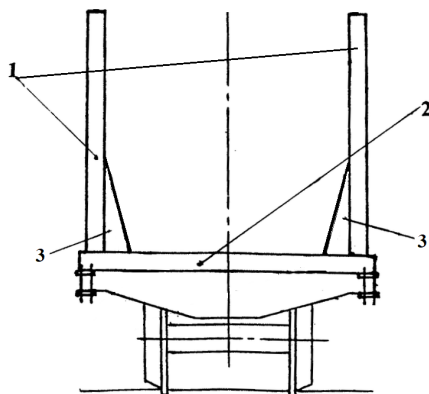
Схема поперечного сечения железнодорожной платформы со стойками, ограждающими штабель круглых лесоматериалов (1 – стойки, ограждающие штабель круглых лесоматериалов; 2 – поперечная балка, к которой крепятся стойки; 3 – ребра жесткости в виде косынок, усиливающих крепление стоек)
